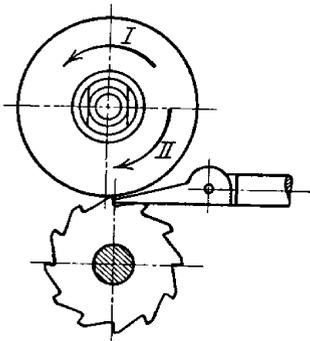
Umlaufrichtung der Scheibe beim Fräterschleifen mit Zunge.
